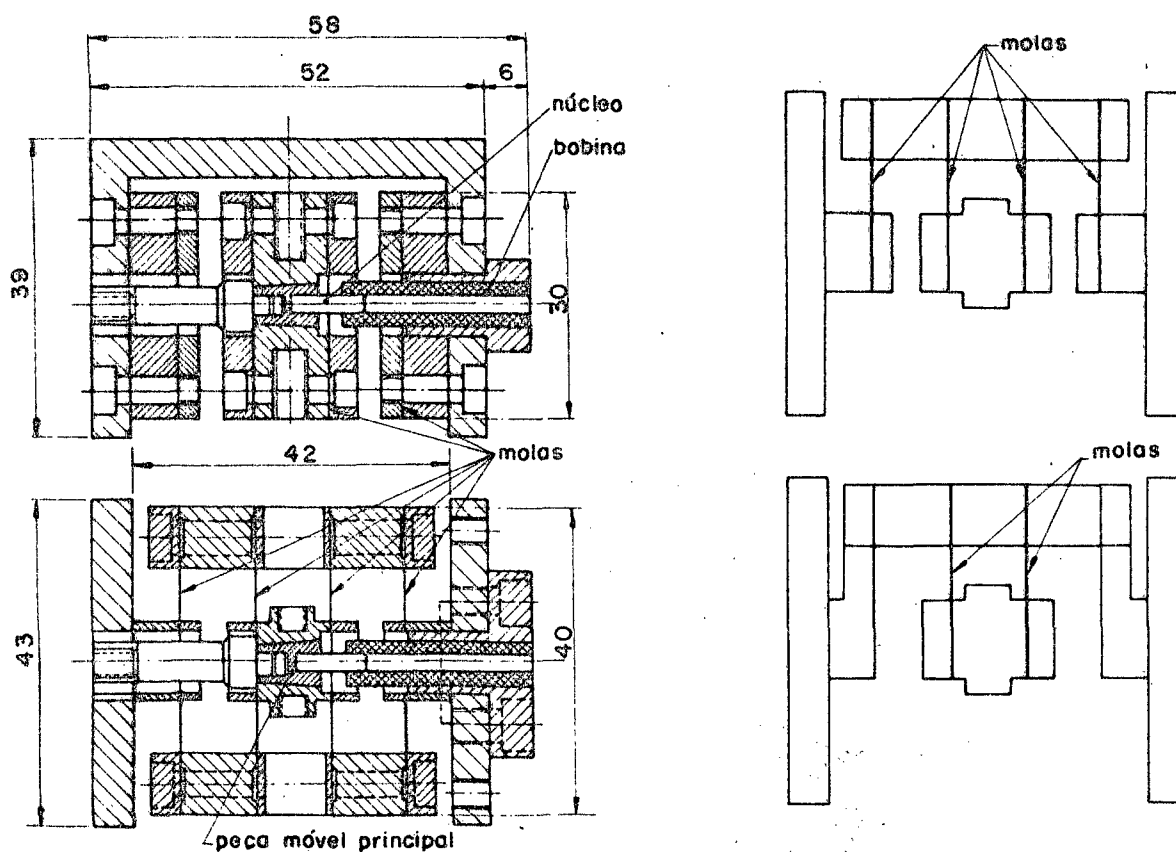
a) projeto do apalpador; b) opção de montagem; c) opção de montagem.
